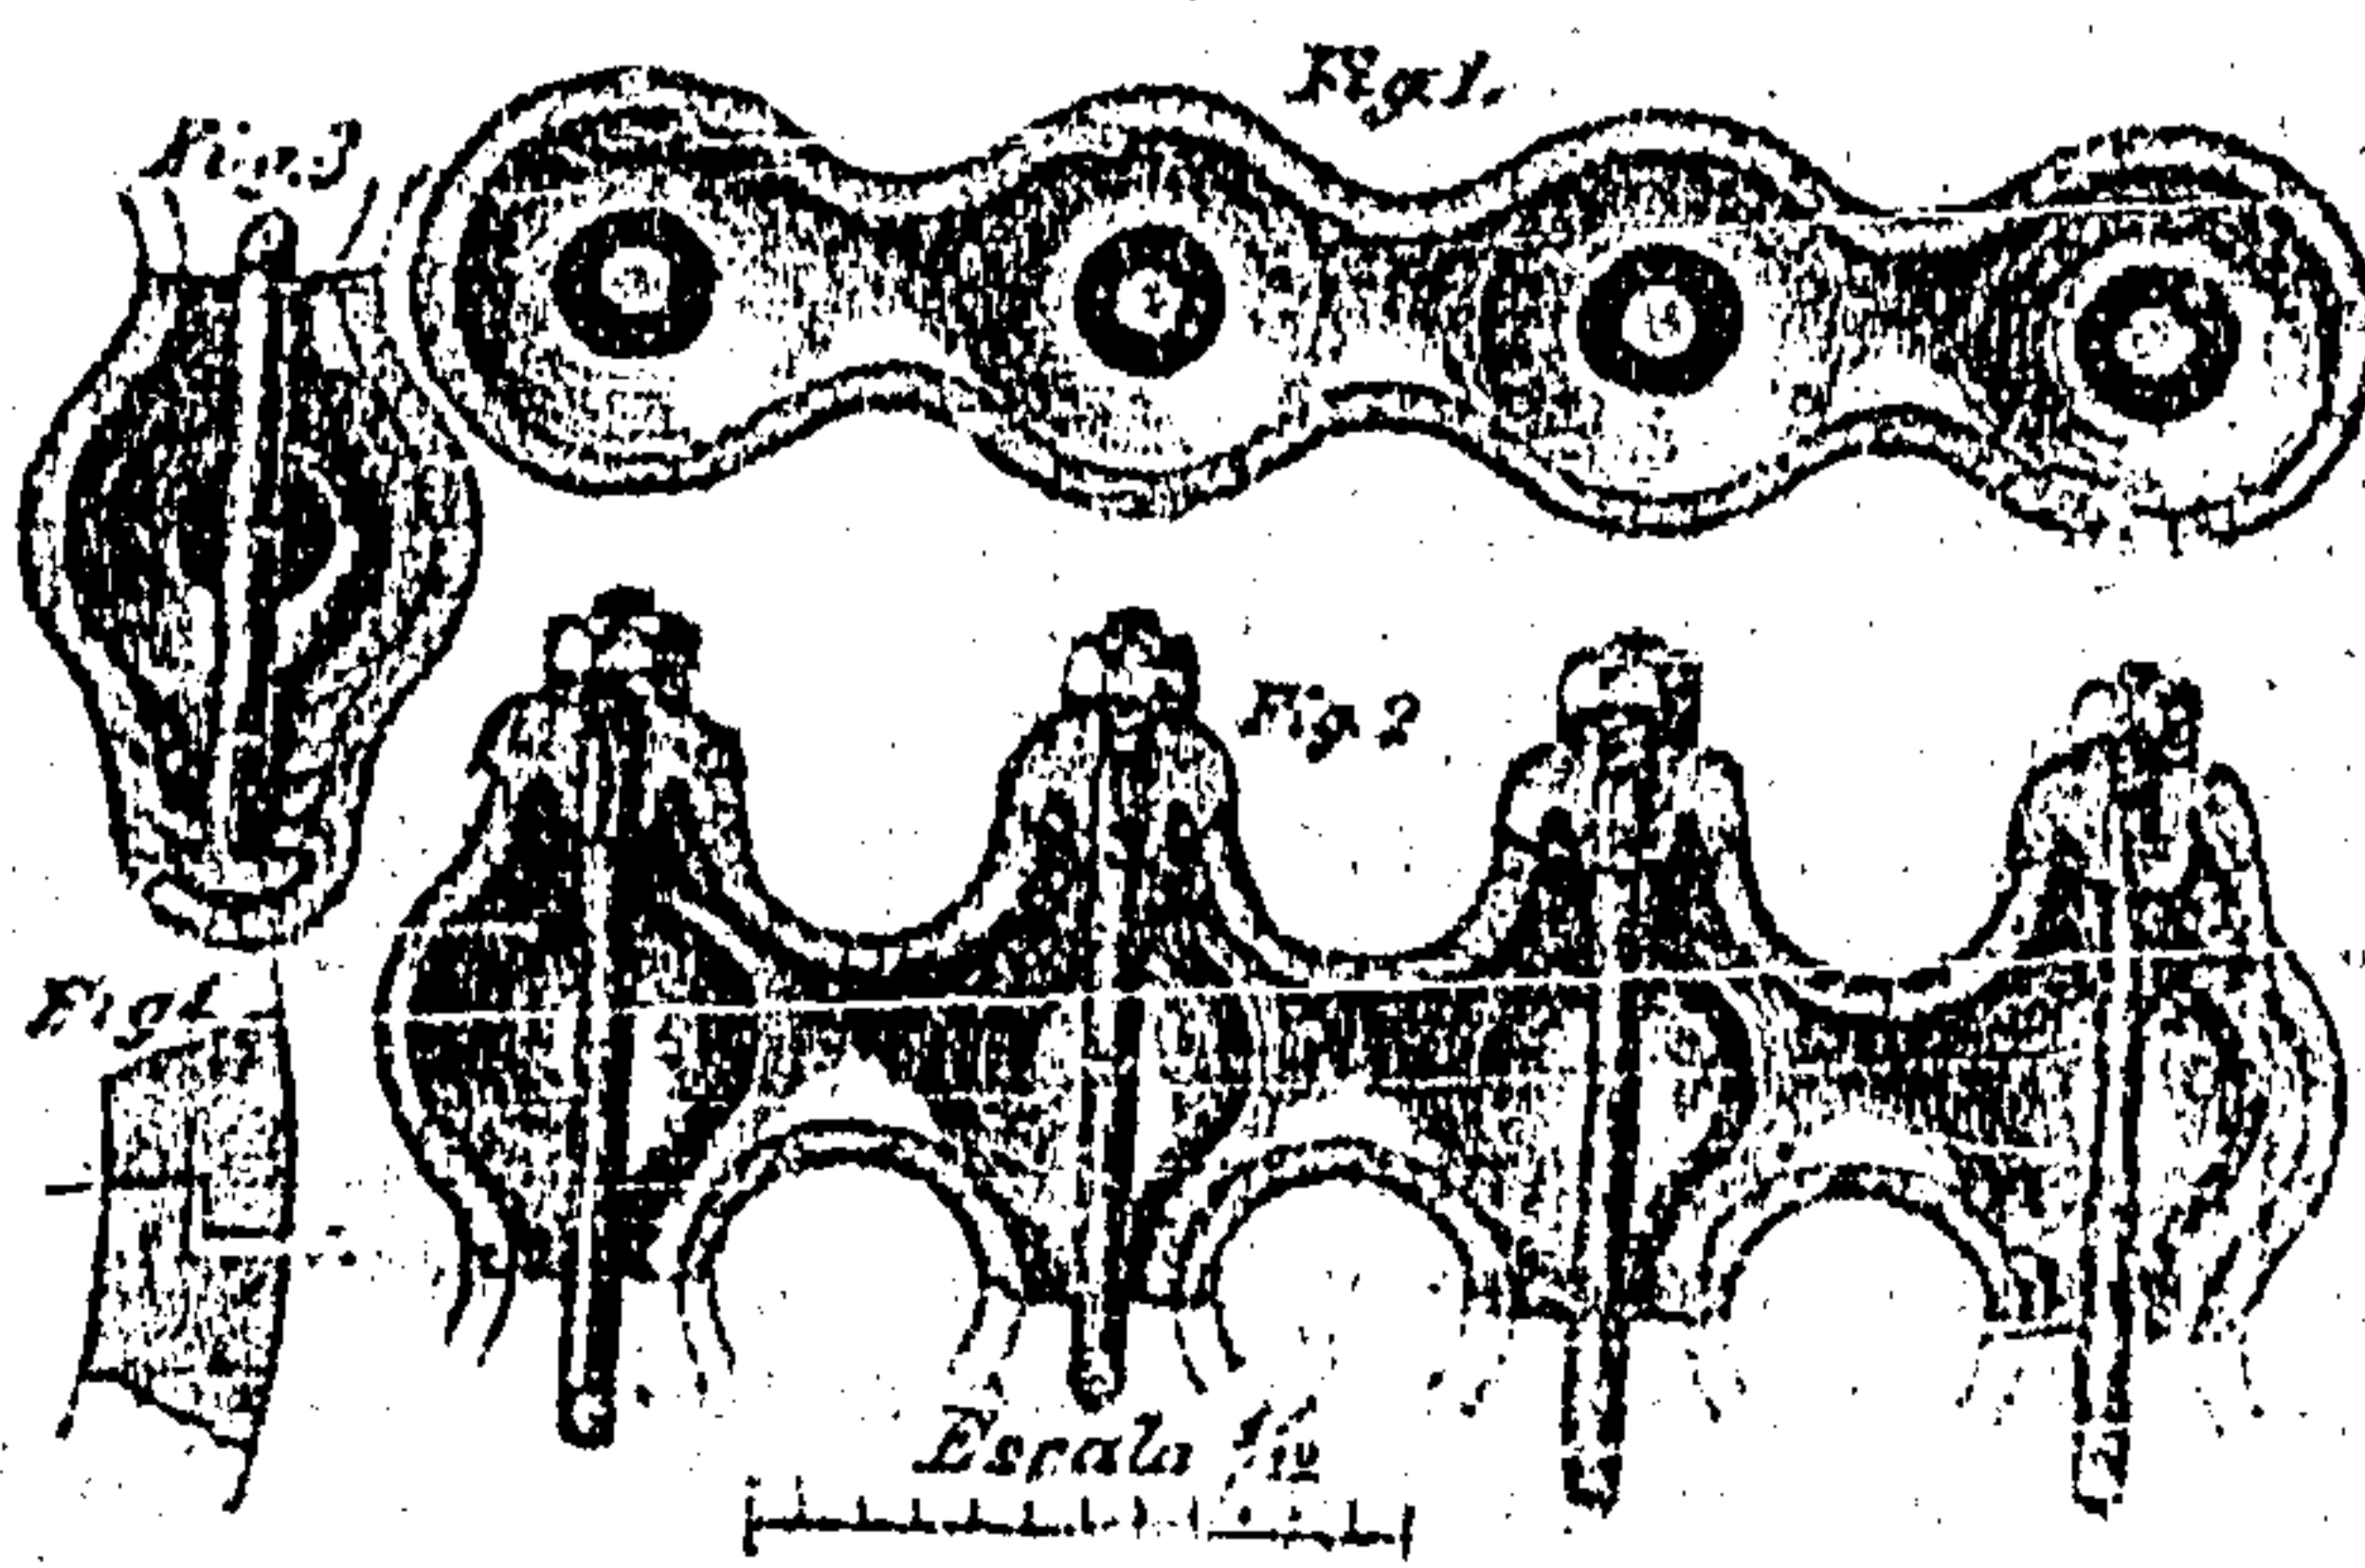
Sección transversal. Fig. 2. Plano longitudinal. Fig. 3. Detalle de la Juntura. Mitad del tamaño. Fig. 4. Sección de la Juntura. Mitad del tamaño.
